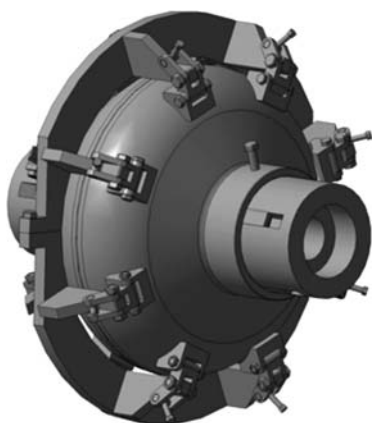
Оснастка для сварки полукамер резонаторов
